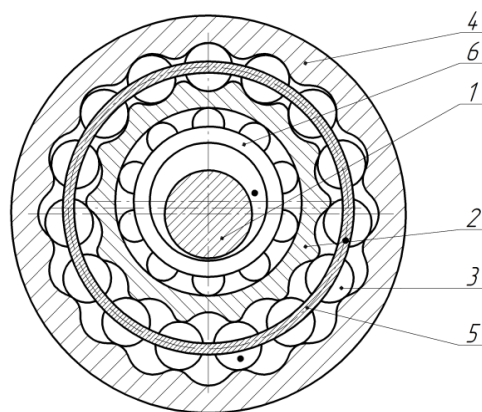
Передача с промежуточными телами качения и свободной обоймой: 1 – входной вал с эксцентриком (генератор); 2 – кулачок; 3 – промежуточные тела качения; 4 – венец; 5 – сепаратор; 6 – подшипник качения.
